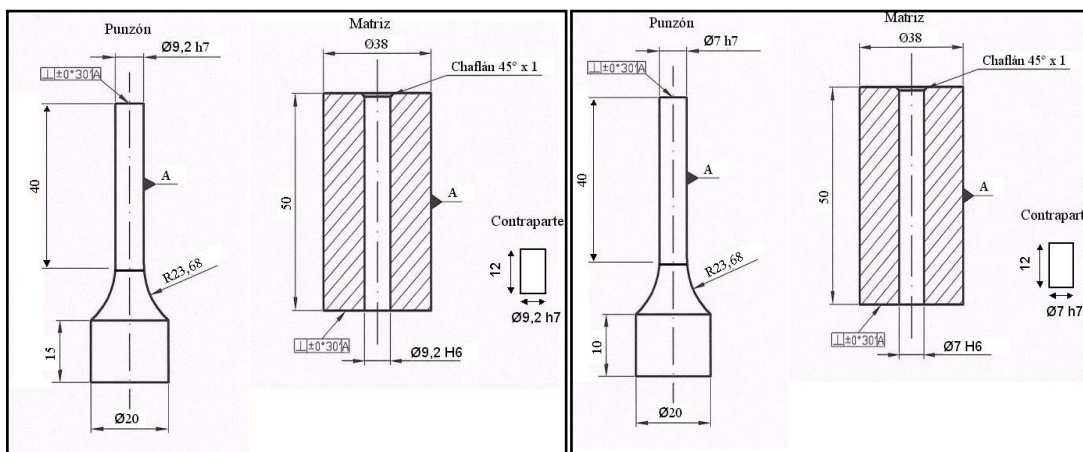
Planos de los conjuntos de diámetros 9,2mm y 7mm
